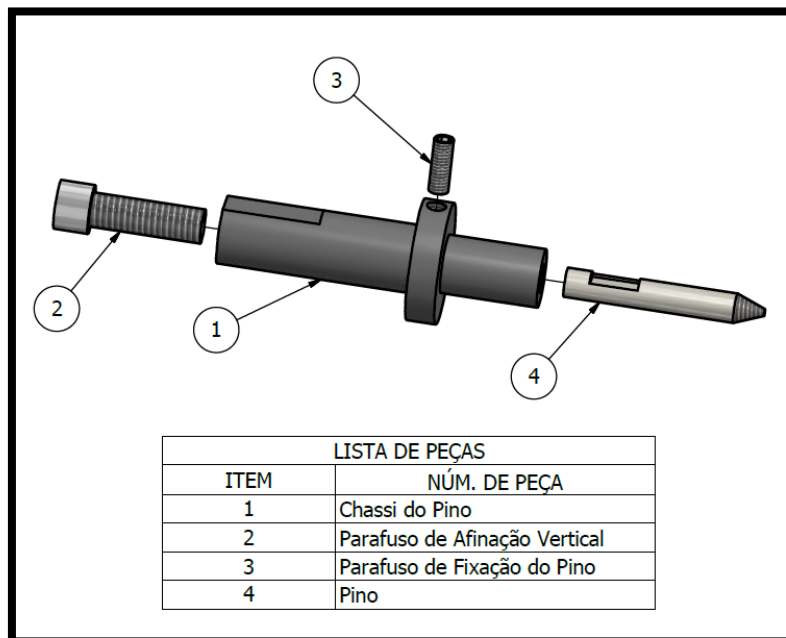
Vista explodida do Pino da Ferramenta com a nomenclatura dos vários componentes constituintes.
